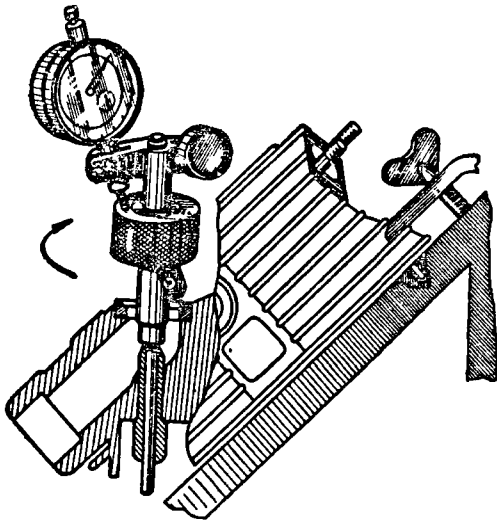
Приспособление для проверки concentричности седла клапана с направляющей втулкой
